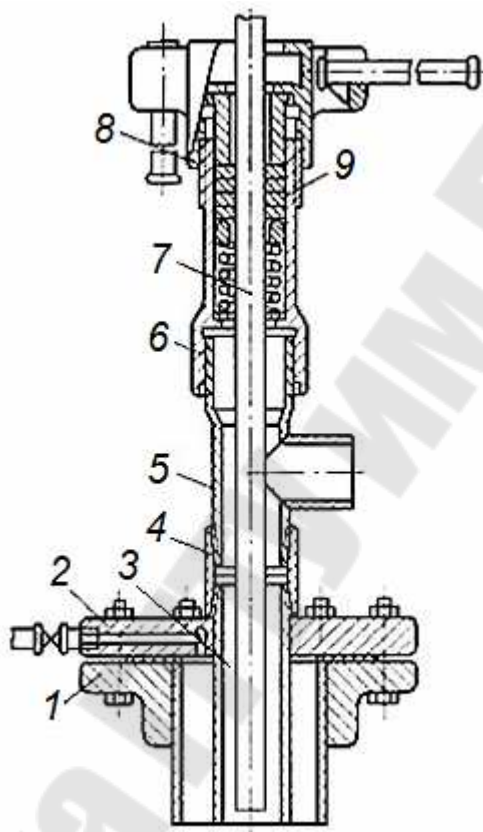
Типичное оборудование устья скважины для штанговой глубиннонасосной установки: 1 – колонный фланец; 2 – планшайба; 3 – НКТ; 4 – опорная муфта; 5 – тройник, 6 – корпус сальника, 7 – полированный шток, 8 – головка сальника, 9 – сальниковая набивка
